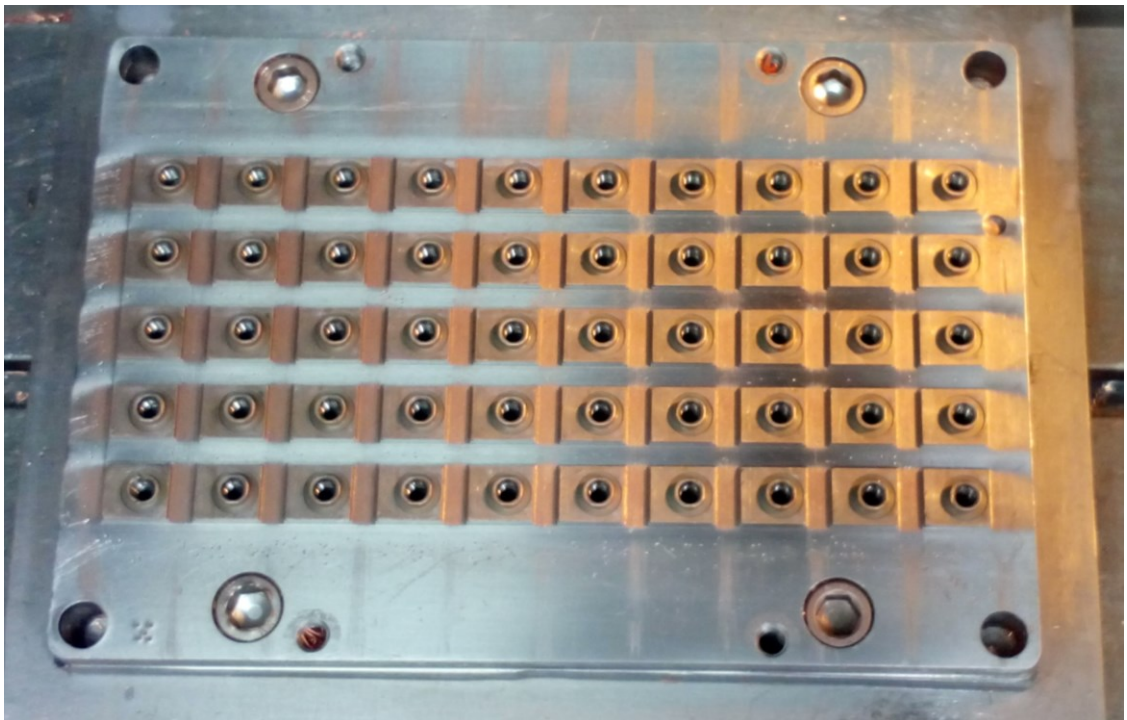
Pásky upevněné v přípravku k operaci vrtání
